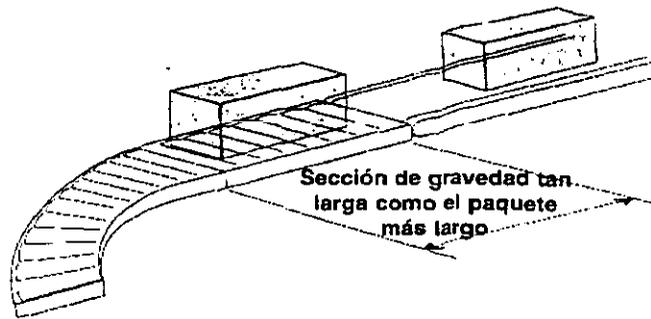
Sección de Gravedad al Largo del Paquete.
